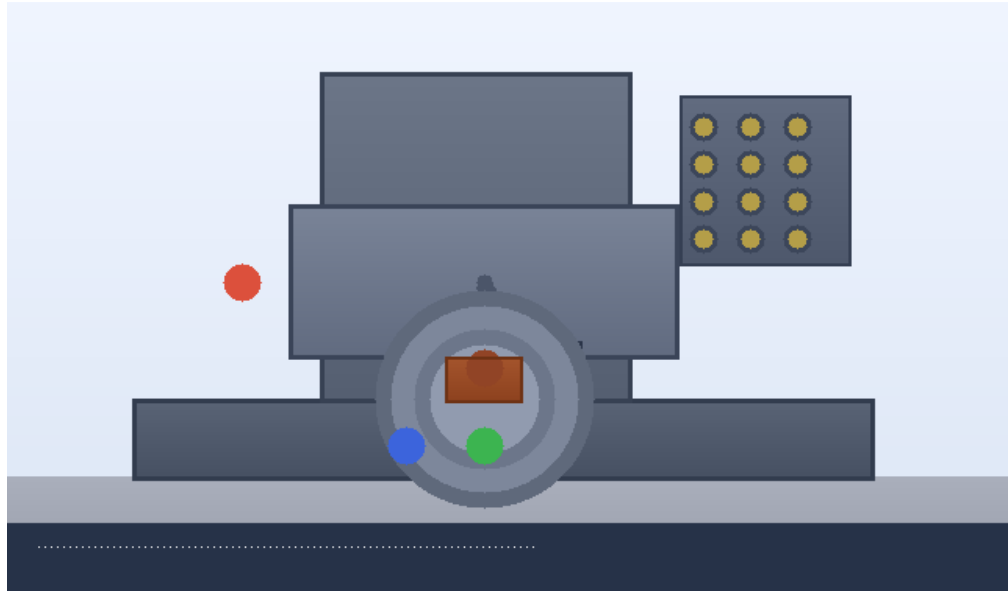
П'ятиосьовий обробний центр: 1 – колона; 2 – шпиндельна бабка з нахилиючою головою (вісь А); 3 – магазин інструментів; 4 – поворотно-нахилиючий стіл (осі В та С); 5 – заготовка складної форми
